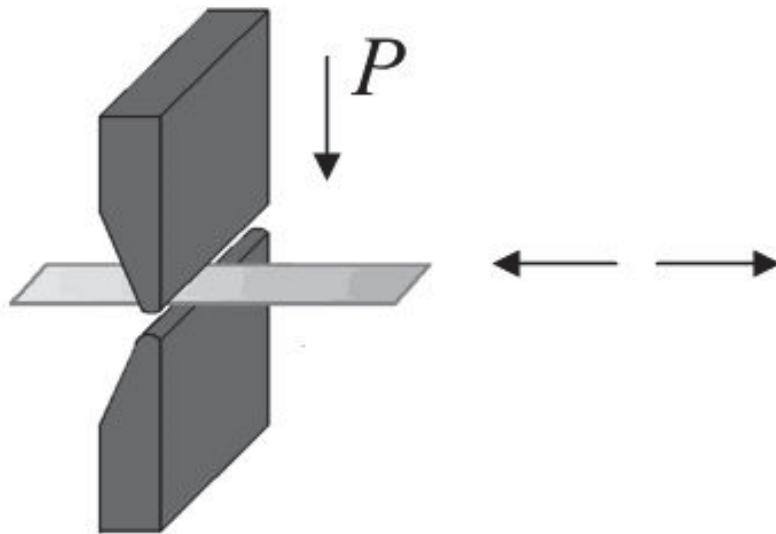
Схема деформирования ленточной заготовки двумя инденторами
